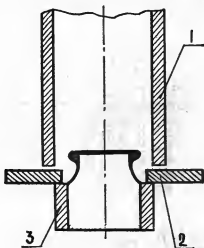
Запрессовка колпачка: 1 — трубка; 2 — шайба; 3 — колпачок.
